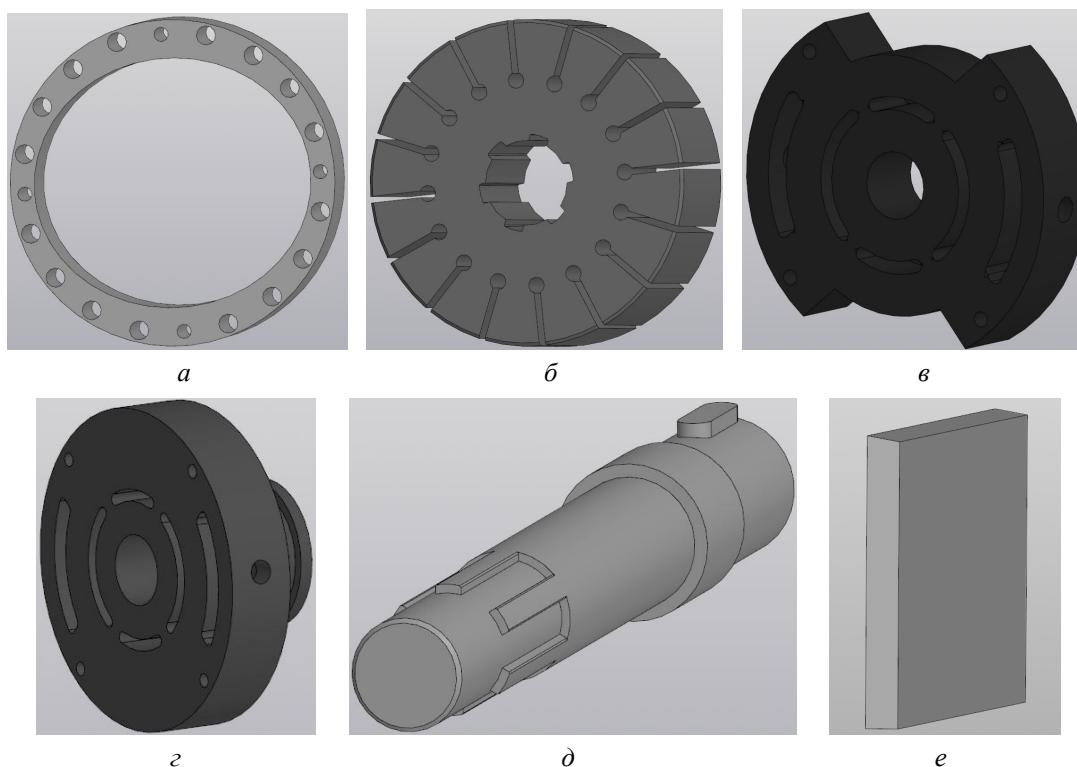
Детали конструкции пластинчатого насоса типа PVV-5 фирмы Bosch Rexroth:
